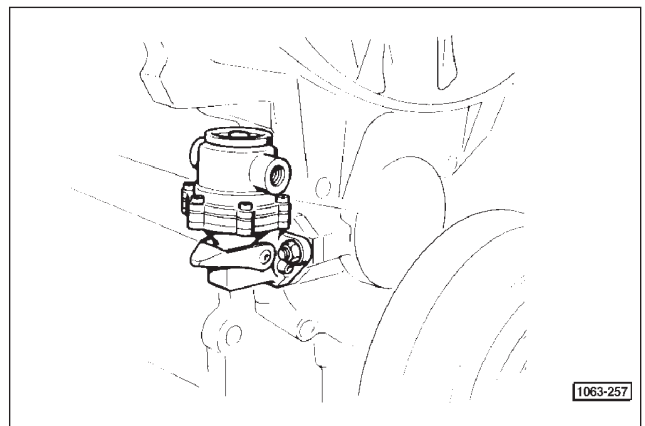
Monter la pompe d'alimentation du carburant, les filtres à gas-oil et, si nécessaire, le préfiltre à gas-oil. Poser la tuyauterie du système d'alimentation.
